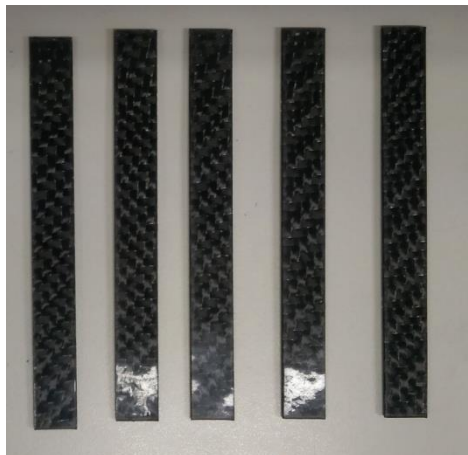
Imagem dos corpos de prova de flexão dos compósitos por moldagem por compressão.
